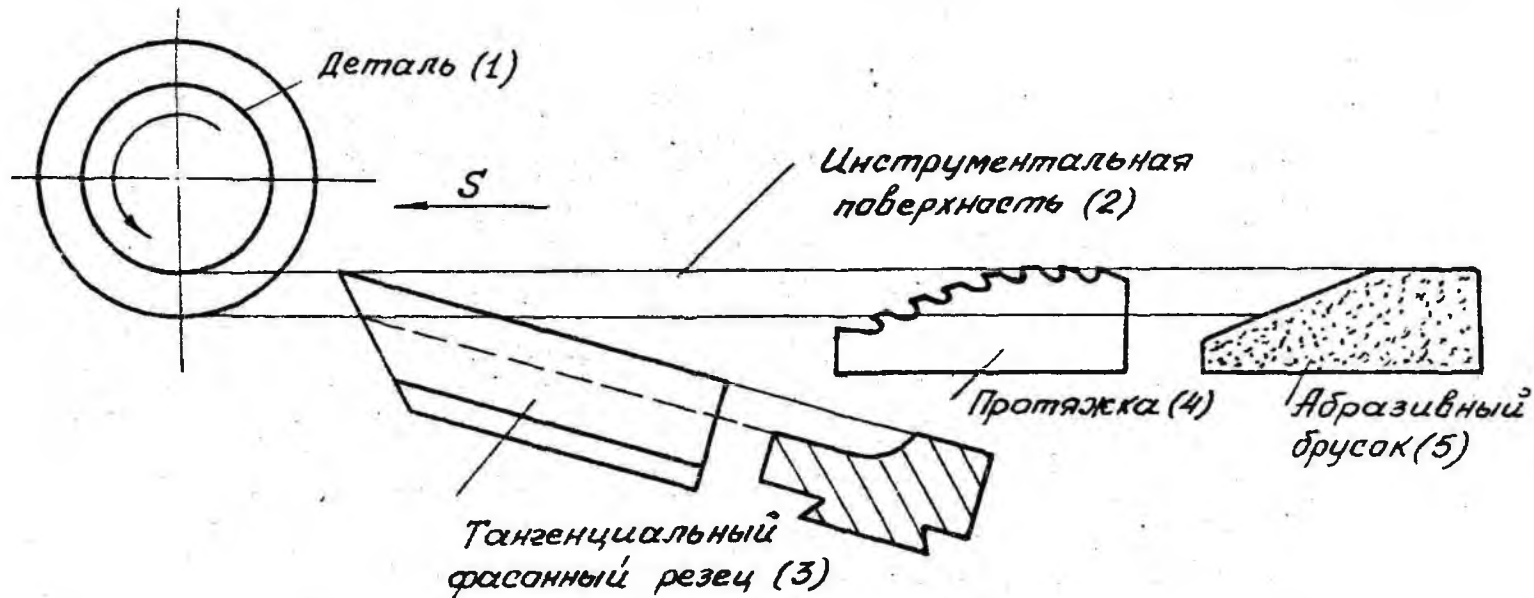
Разные инструменты на базе одной и той же инструментальной поверхности
